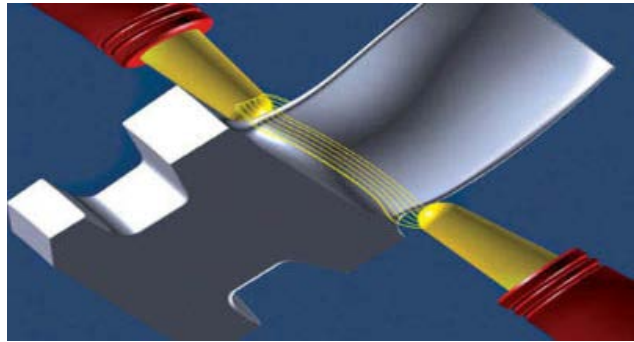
Usinage en roulant 5 axes d'aubes de turbine.
